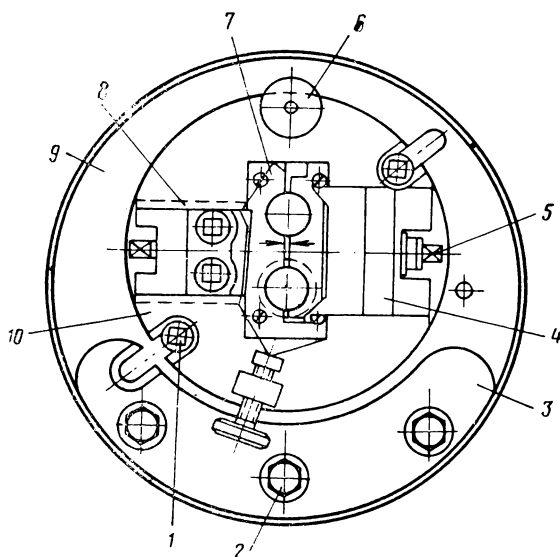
Приспособление для расточки отверстий в корпусе кронштейна щеткодержателя тягового двигателя НБ-412М:
